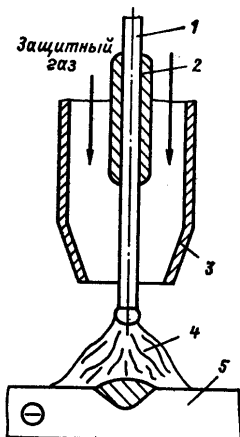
Схема процесса сварки в среде защитных газов плавящимся электродом:
